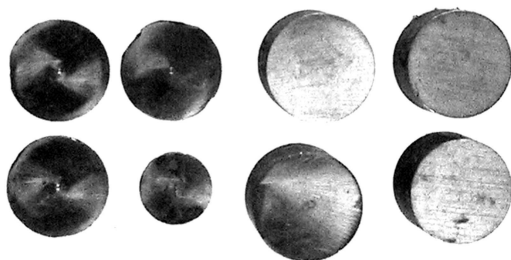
Заготовки магнитов после резки на круга с станках: 1– HSG TECHNOLOGIE; 2– ШАРМ – 3 закреплением зерен
